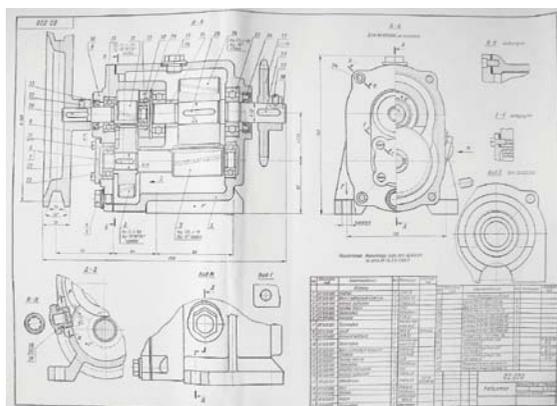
Чертеж редуктора цилиндрического одноступенчатого
